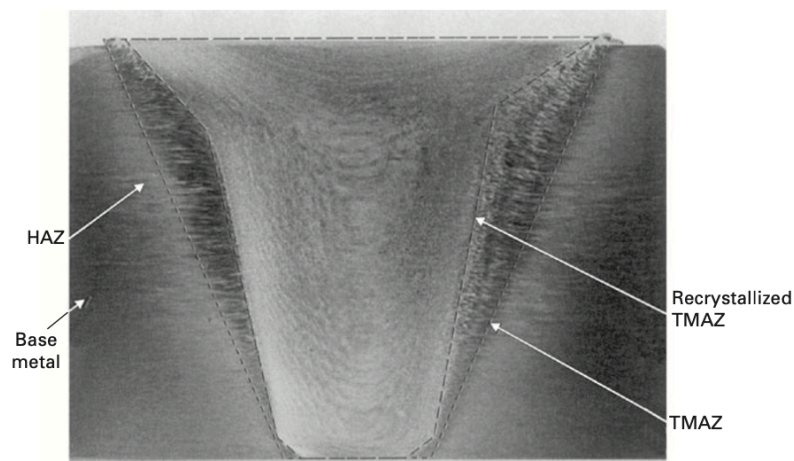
Microestructura de soldadura FSW. [9]
